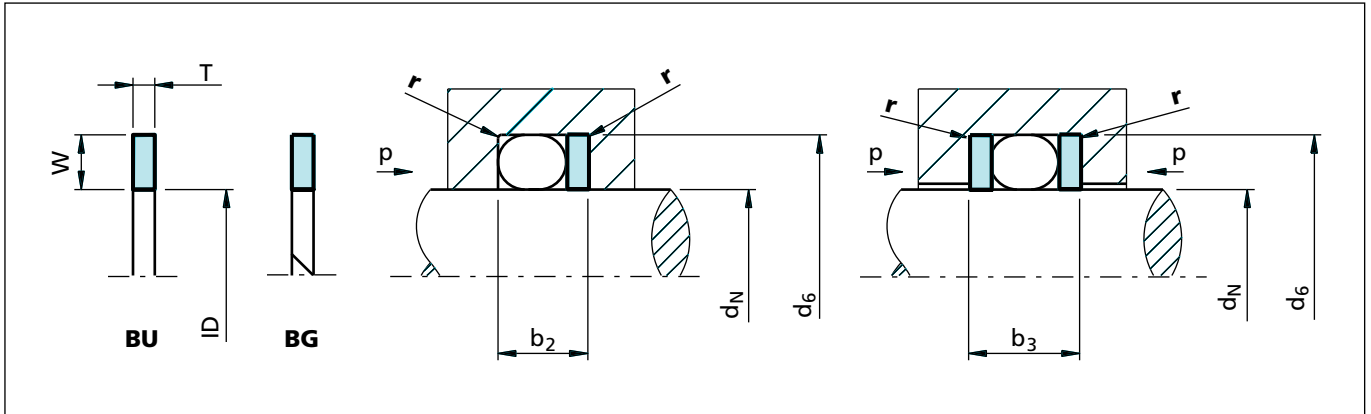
Einbauzeichnung, innendichtend, rechteckige Stützring Bauformen
